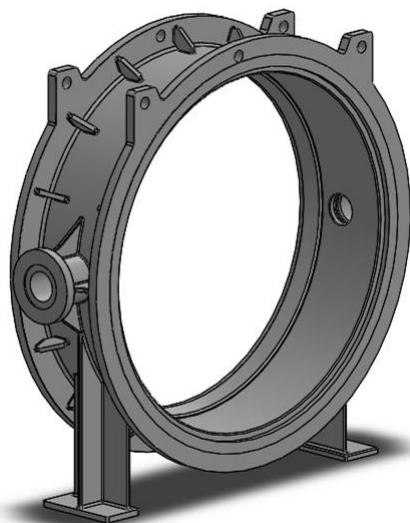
Корпус дискового поворотного затвора с проходным сечением 800 мм
